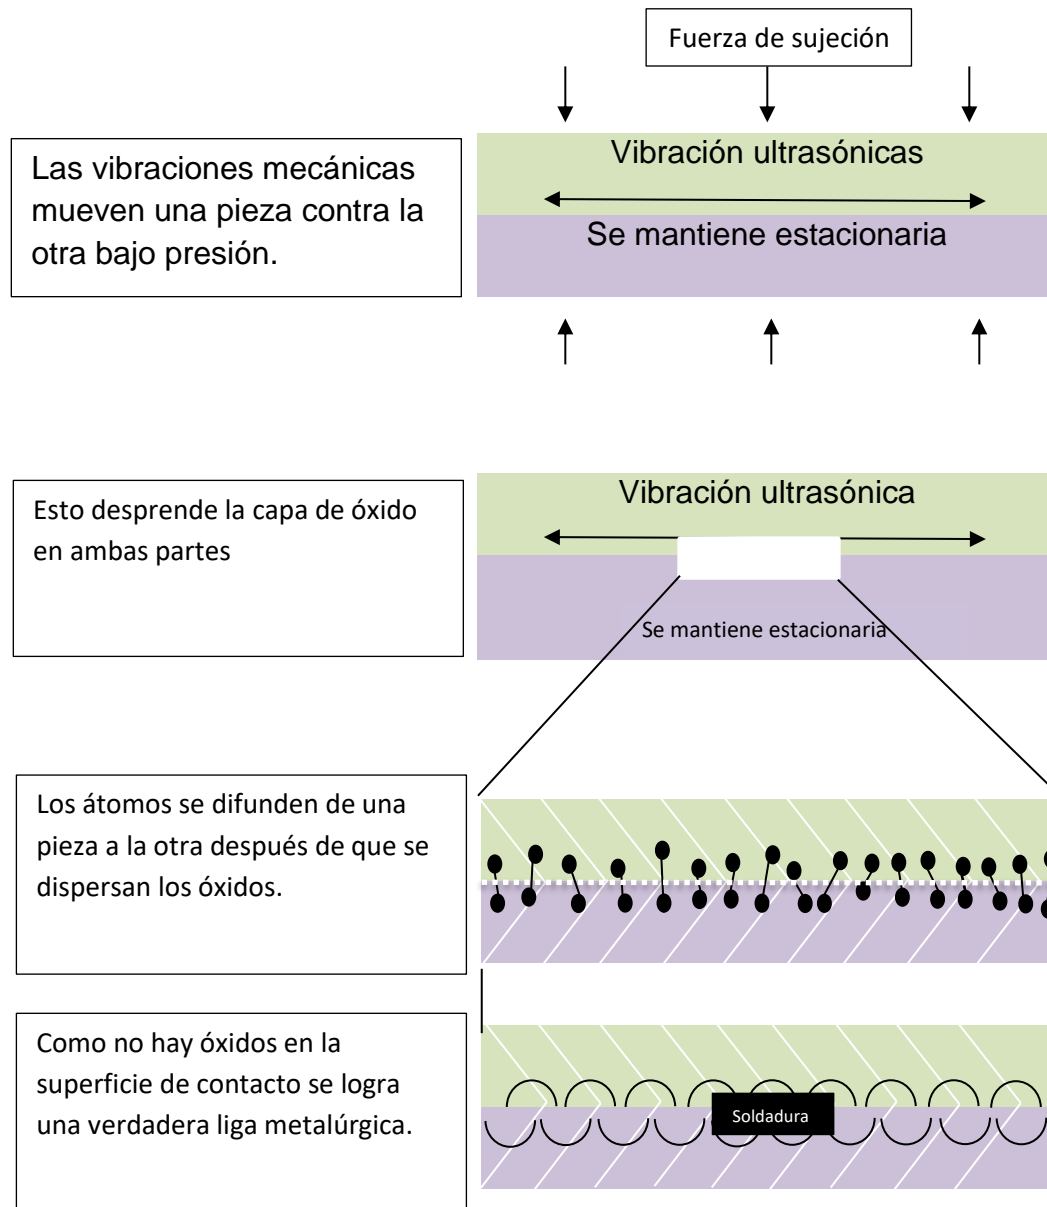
Proceso de unión en soldadura ultrasónica. Fuente [5]
